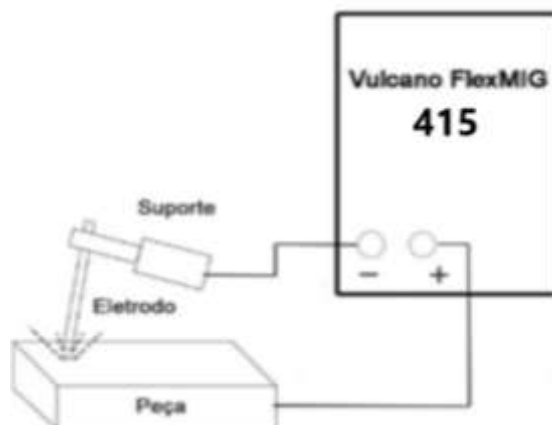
Conexão positiva para soldagem com eletrodo revestido.
